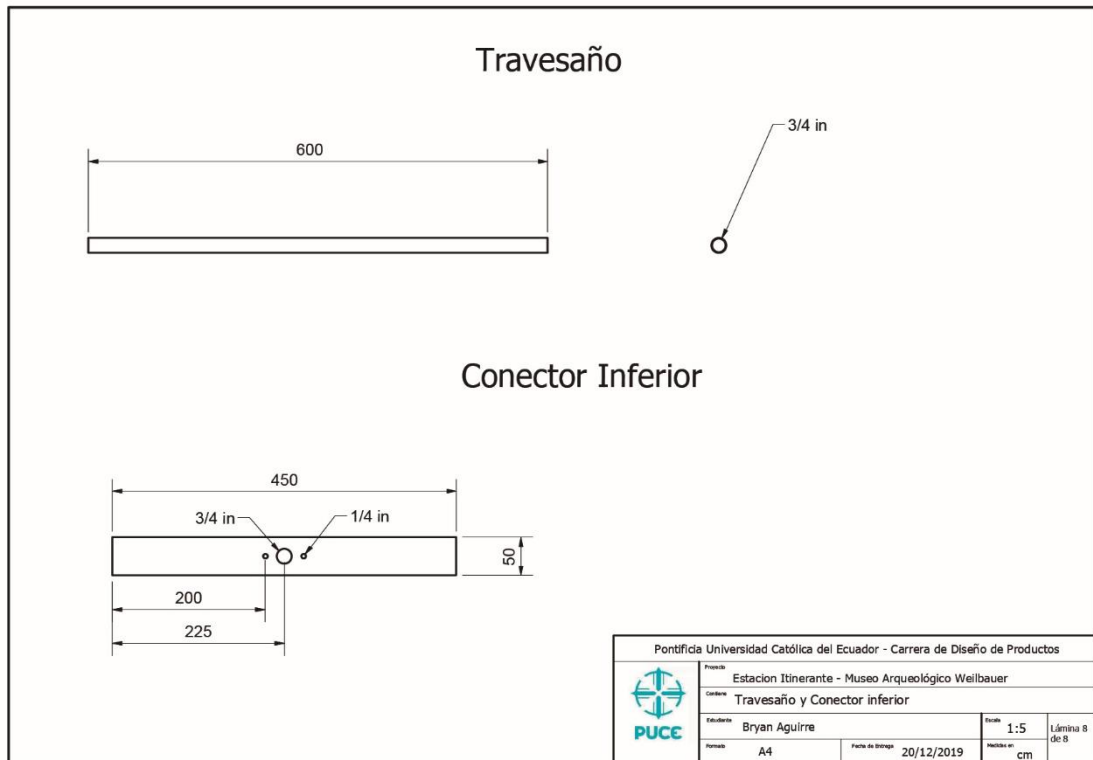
Travesaño y conector inferior para columnas. Fuente elaboración propia.
